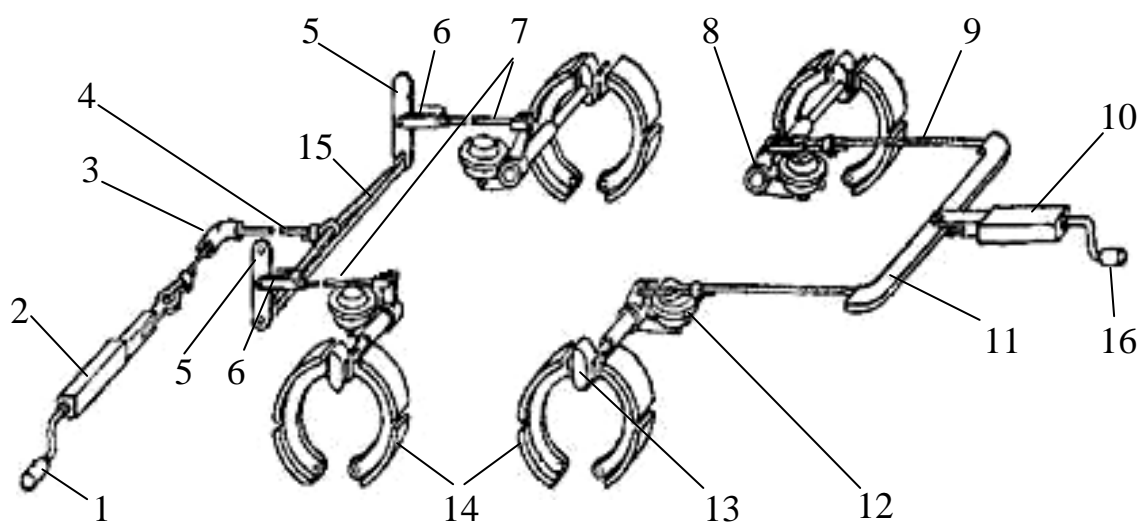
Конструкция стояночного тормоза полуприцепа КАМАЗ: 1 и 13 – рукоятки; 2 и 10 – силовые передачи; 3 – направляющая трубка; 4 – трос переднего тормоза; 5 – рычаги; 6 – вилки; 7 – тяги; 8 – регулировочный рычаг; 9 – трос заднего тормоза; 11 – уравниватель; 12 – тормозная камера; 13 – разжимной кулак; 14 – тормозные колодки; 15 – приводной валик
